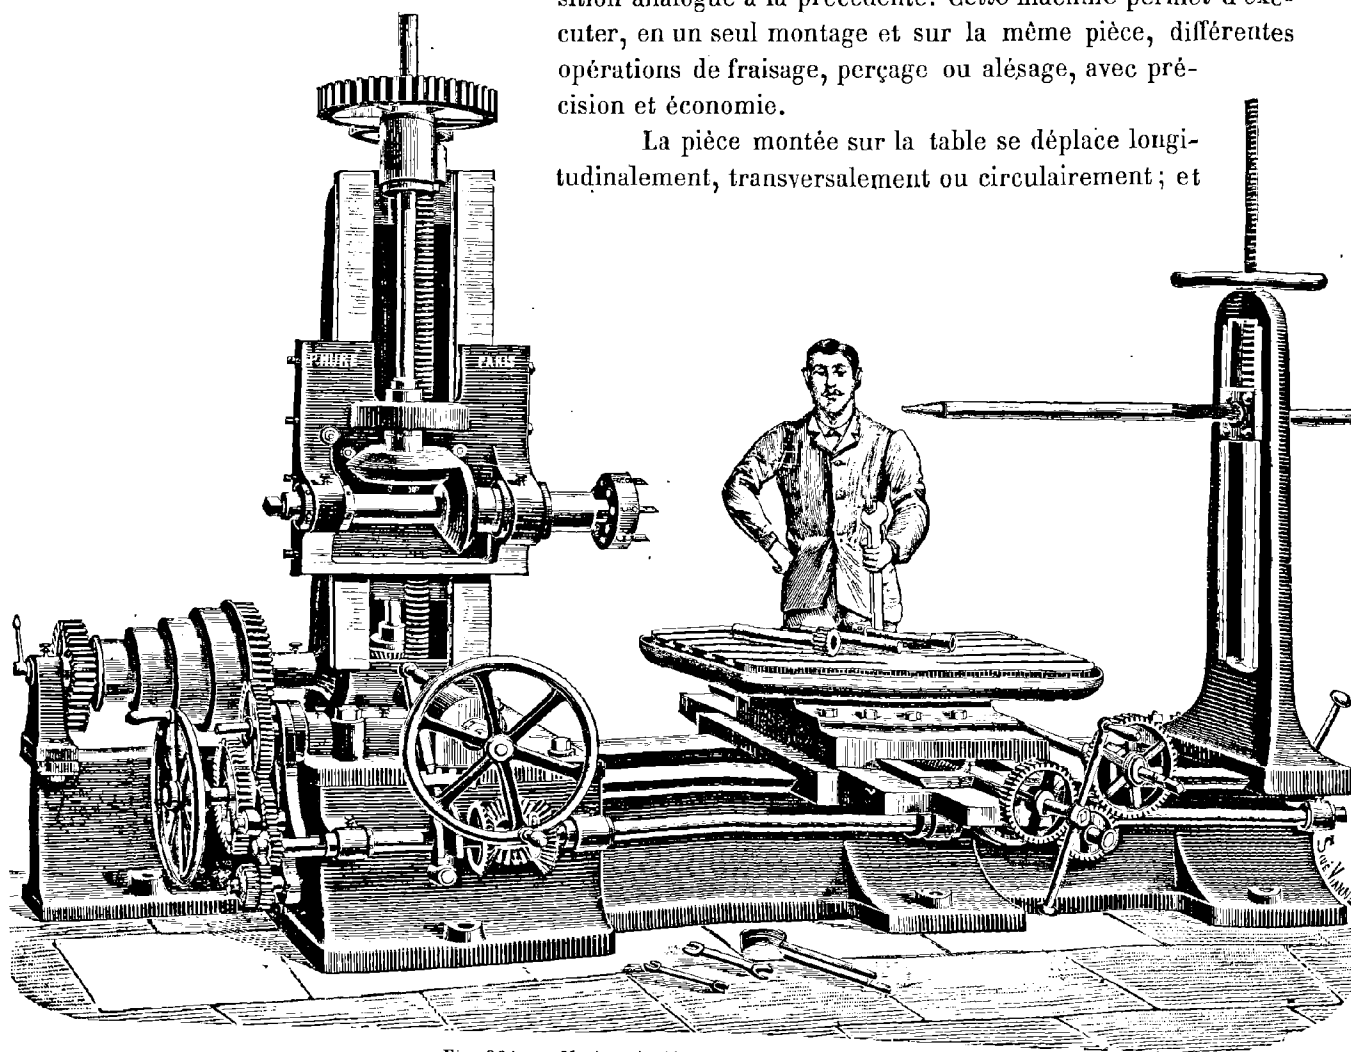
Machine à aléser, percer et fraiser de M. Huré.
